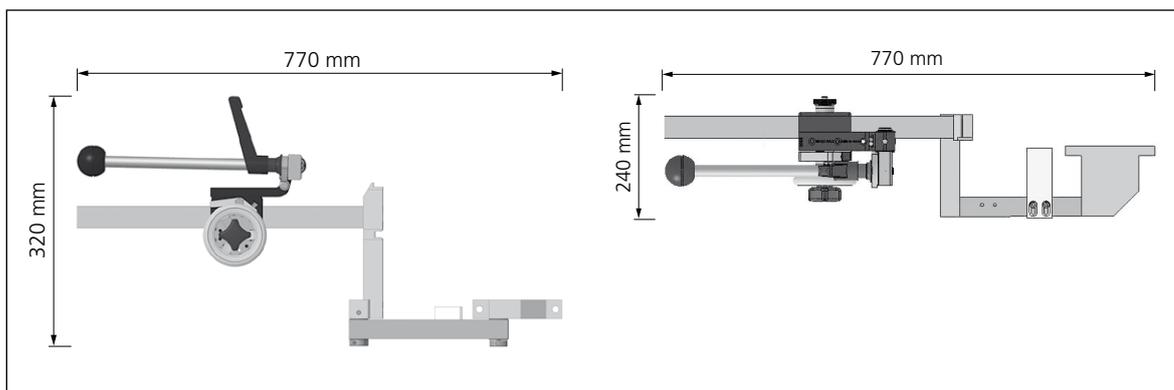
Vista lateral y superior del HV261 (dimensiones en mm)
